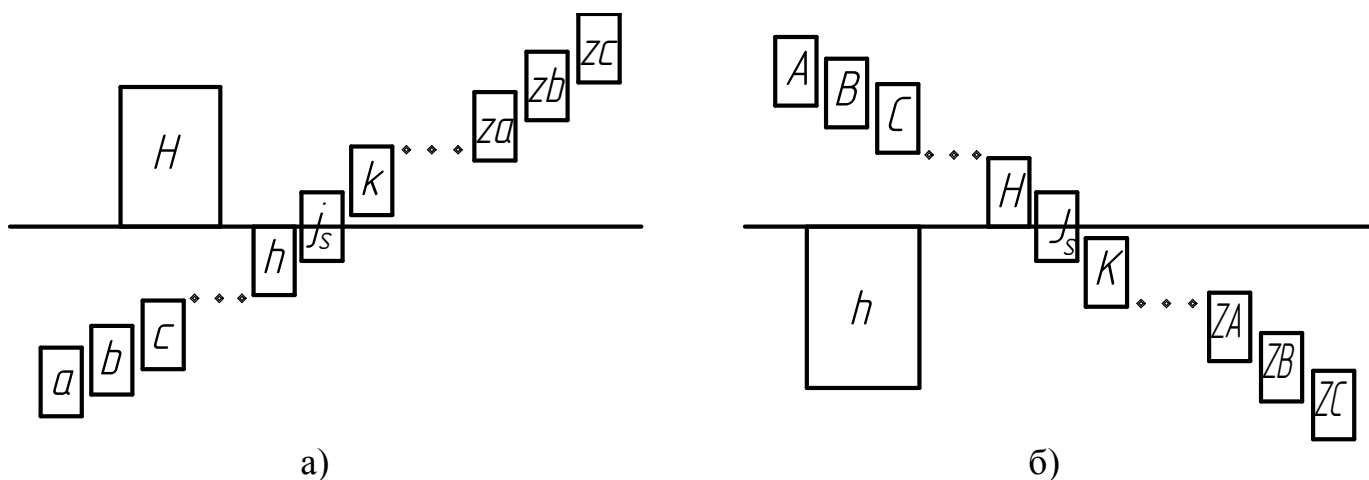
Схемы расположения полей допусков в системе ИСО и ЕСДП; а – система отверстия; б – система вала
